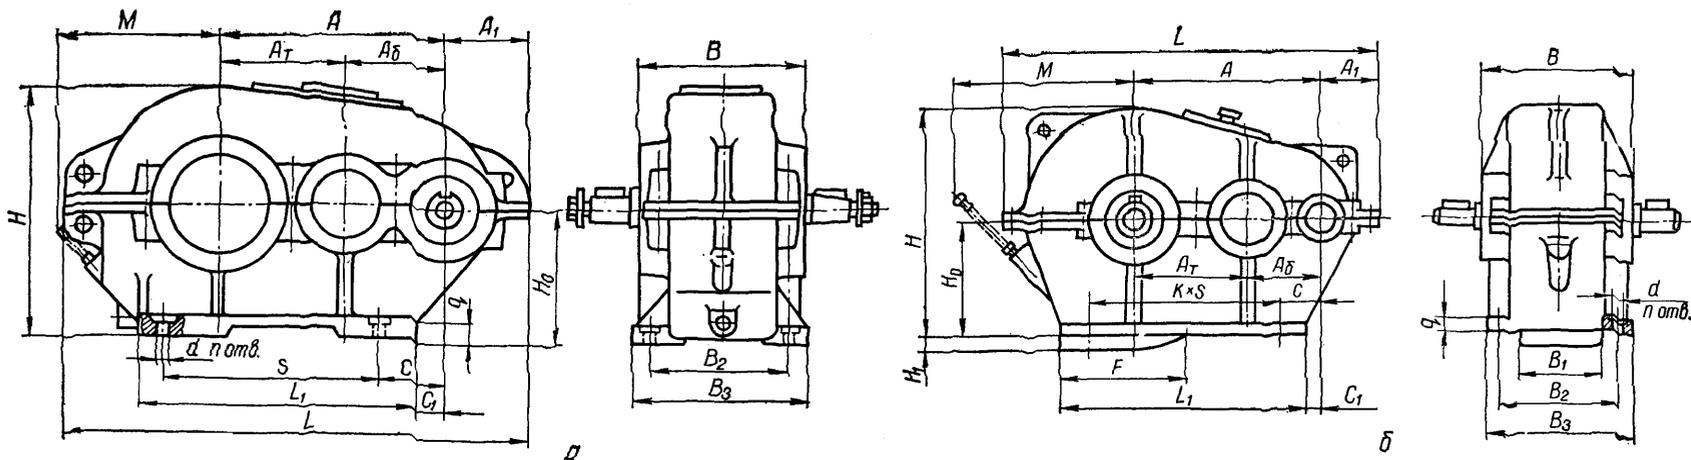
Основные и габаритные размеры редукторов: а — РМ 250Б и РМ 350Б; б — РМ 750Б, РМ 850Б и РМ 1000Б.
